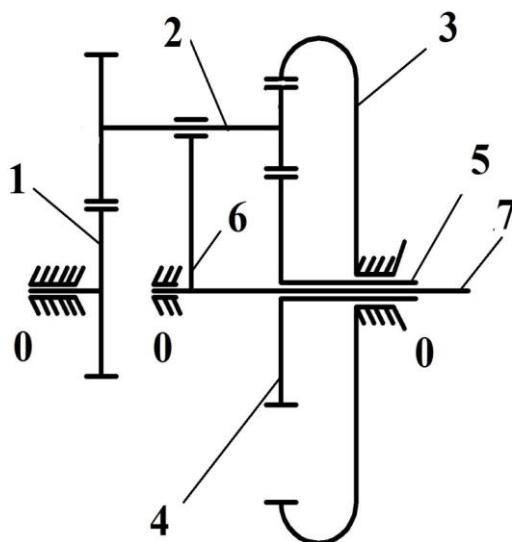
Зубчато-рычажная передача с двумя выходными валами
